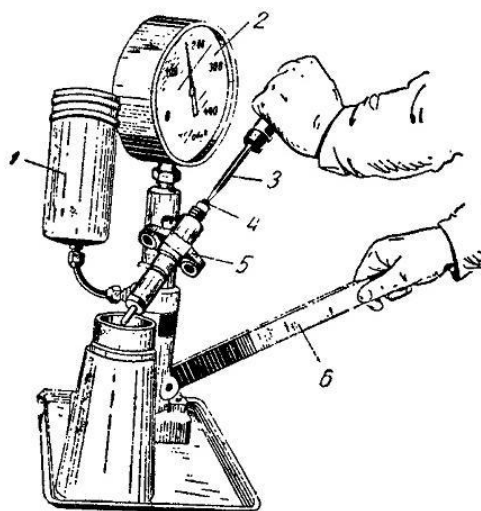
Проверка форсунок с помощью прибора КИ-562-ГОСНИТИ:
